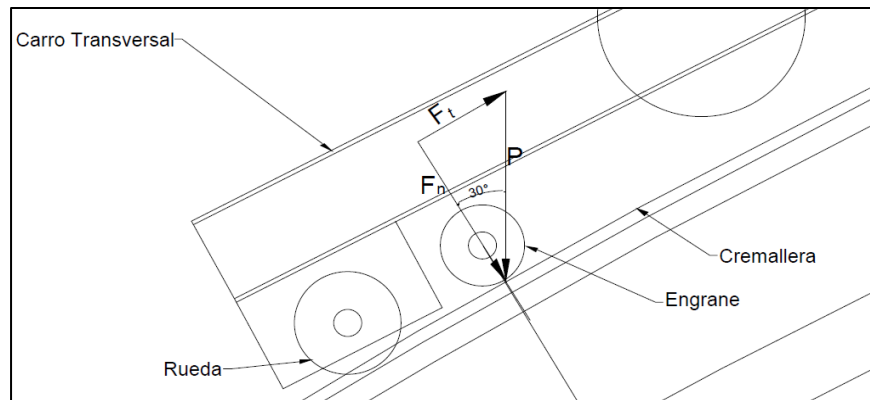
DCL Diseño Sistema Engrane-Corona
